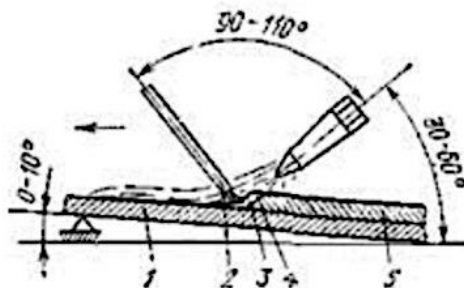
Схема газопламенной наплавки с внешней подачей присадочного прутка:
